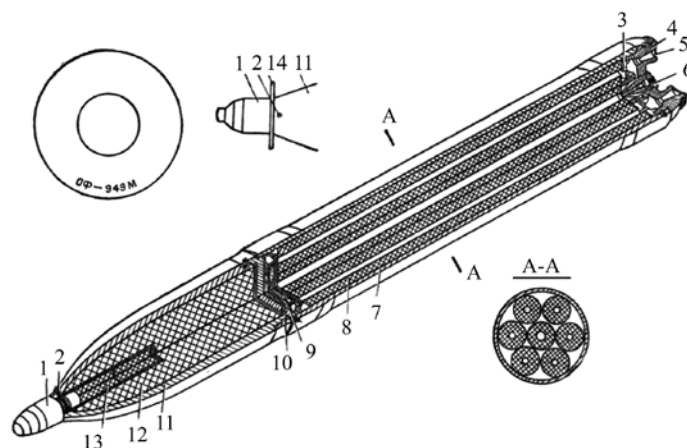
140-мм турбореактивный осколочно-фугасный снаряд М-14-ОФ: 1 — взрыватель; 2 — винт стопорный; 3 — диафрагма; 4 — сопловое дно; 5 — герметизирующее кольцо; 6 — свеча; 7 — ракетная камера; 8 — пороховой заряд; 9 — воспламенитель; 10 — дно; 11 — корпус головной части; 12 — разрывной заряд; 13 — дополнительный детонатор; 14 — тормозное кольцо
